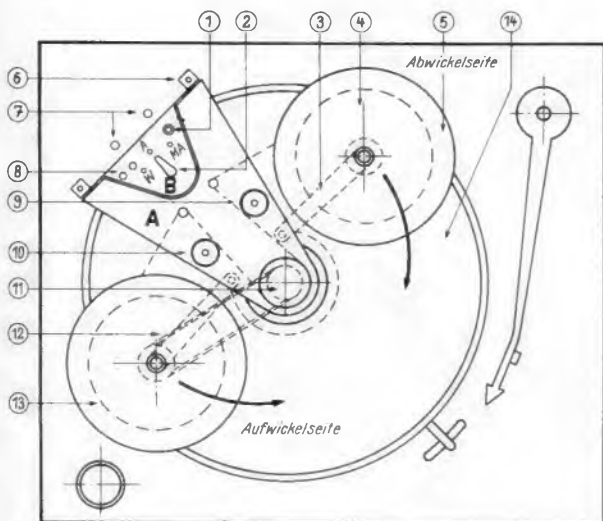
Aufsicht auf den Adapter. Teil B ist mit Winkeln fest auf dem Plattenspielerboden montiert, Teil A läßt sich hochklappen. 1 = Netzschalter, 2 = Umschalter, 3 = Steg, 4 = Filz, 5 = Spulenaufplateteller, 6 = Befestigungswinkel, 7 = Durchführungsloch, 8 = Mikrofonanschluß, 9 = Löschkopf, 10 = Kombikopf, 11 = Tonrolle, 12 = Gummiantriebsriemen, 13 = Spulenaufplateteller, 14 = Plattenteller
